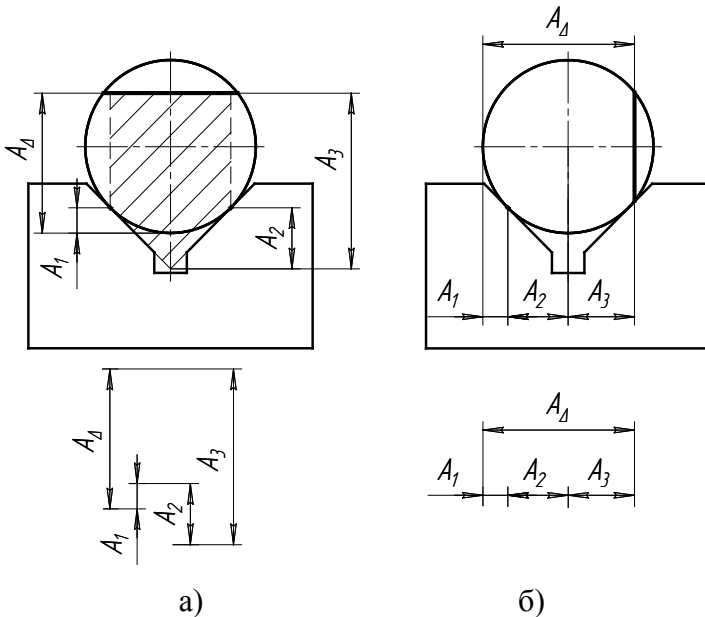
Жорстка опорна призма і розмірні ланцюги для визначення похибки базування при фрезеруванні лиски:
